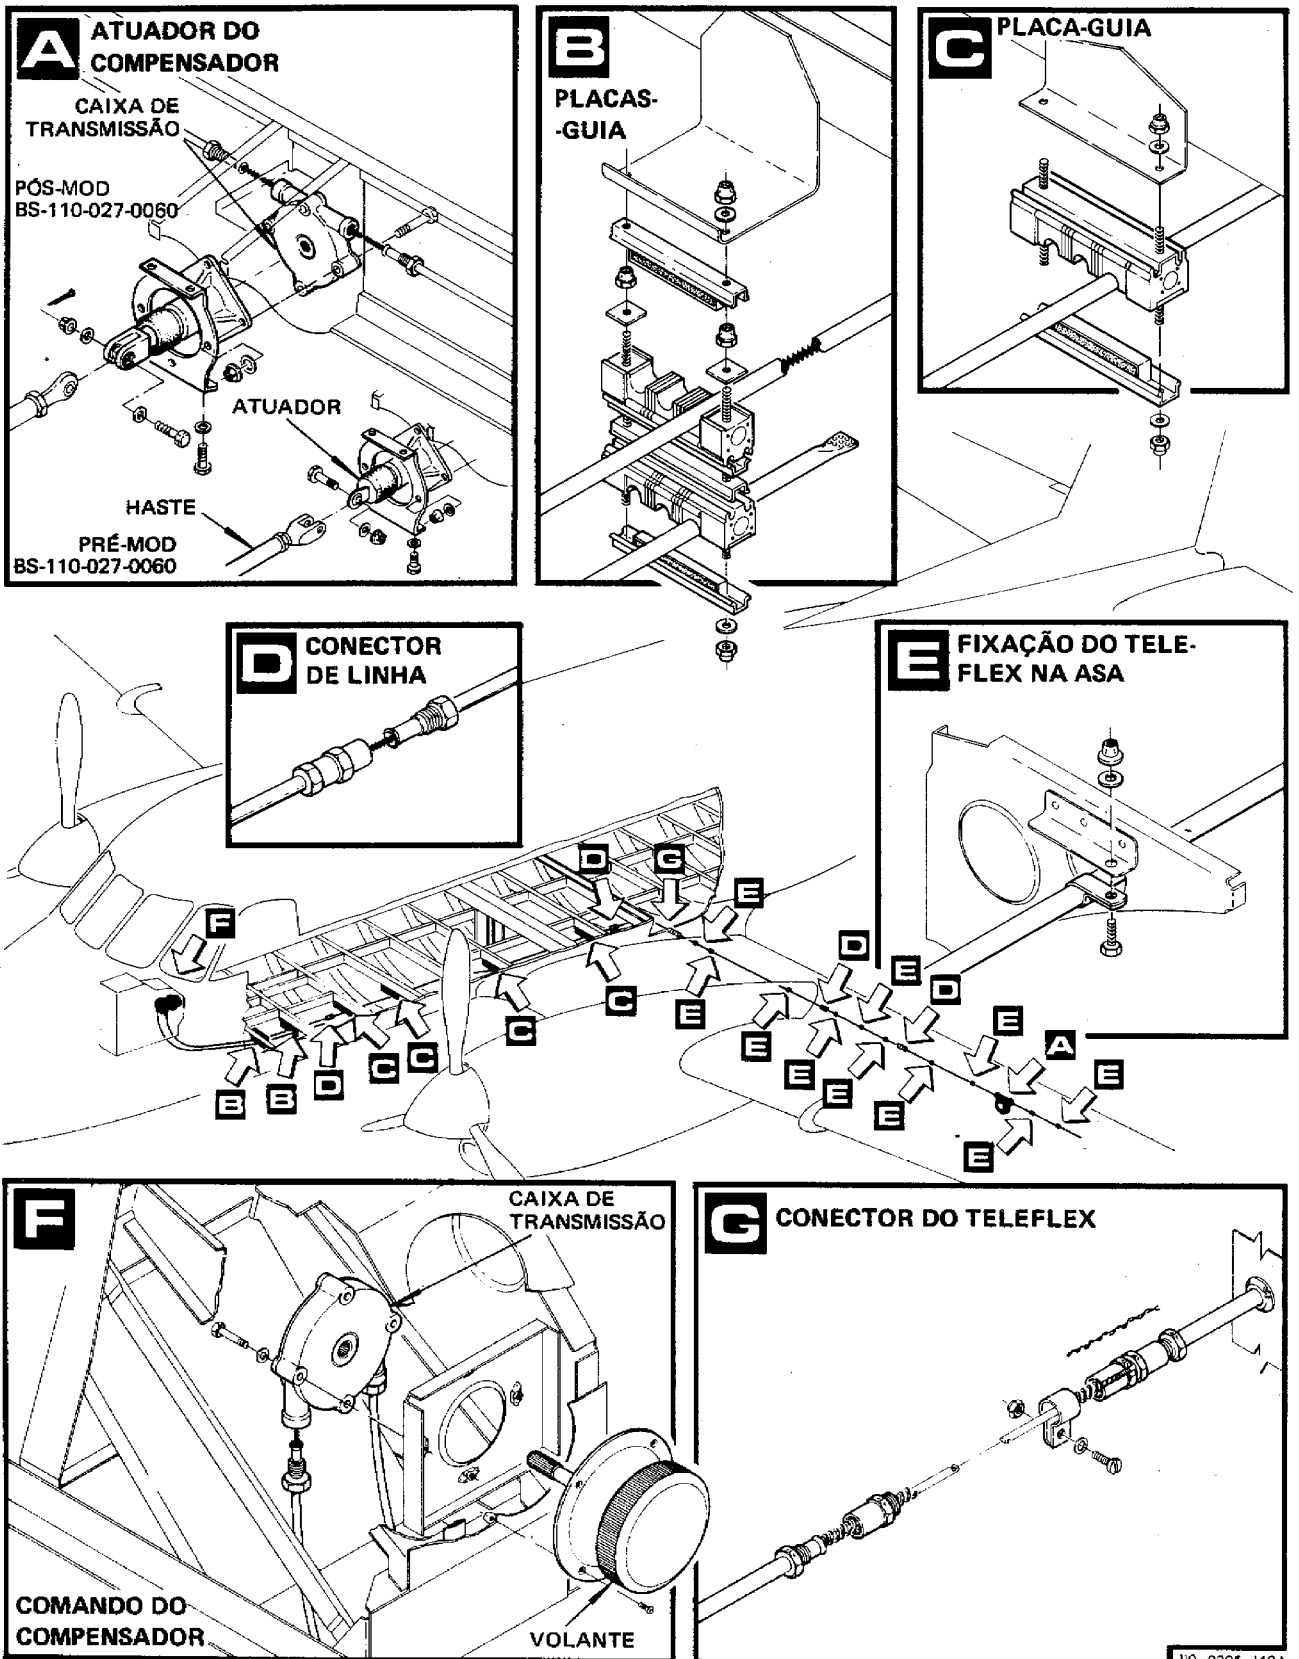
Remoção/Instalação do Sistema de Comando do Compensador do Aileron
